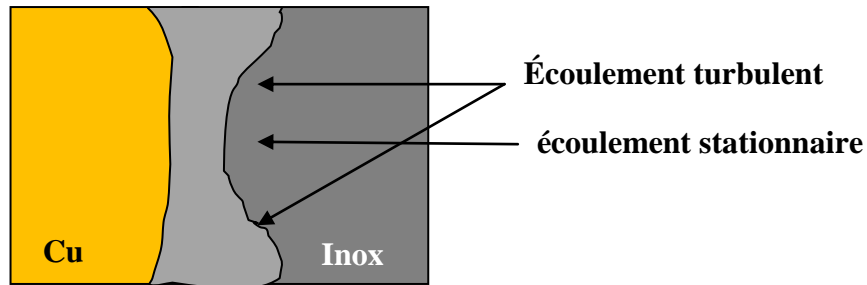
Le régime d'écoulement dans les différentes parties de soudure.
